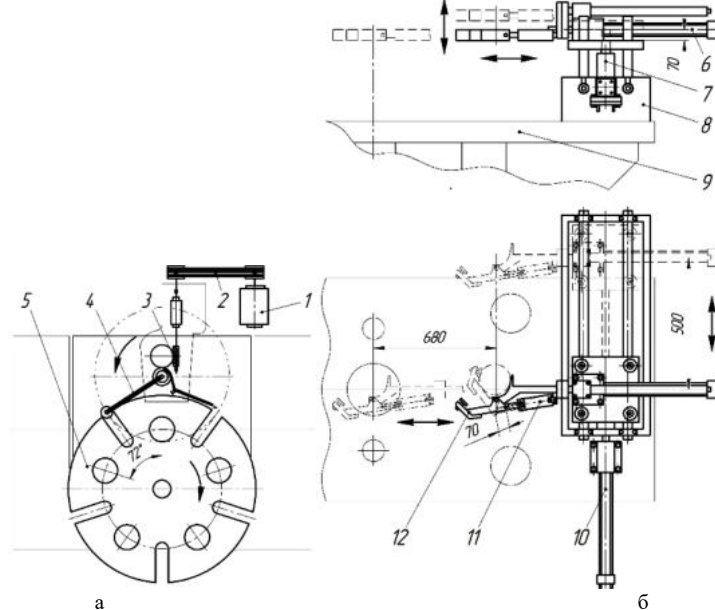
Схемы автоматической подачи полуфабрикатов гильз с помощью револьверного стола (а) и гидравлического манипулятора (б): 1 – электродвигатель; 2 – ременная передача; 3 – червячный редуктор; 4 – рычаг; 5 – револьверный стол; 6 – цилиндр подачи; 7 – цилиндр подъема; 8 – основание; 9 – стол пресса; 10 – цилиндр перемещения; 11 – цилиндр захвата; 12 – клещевой захват
